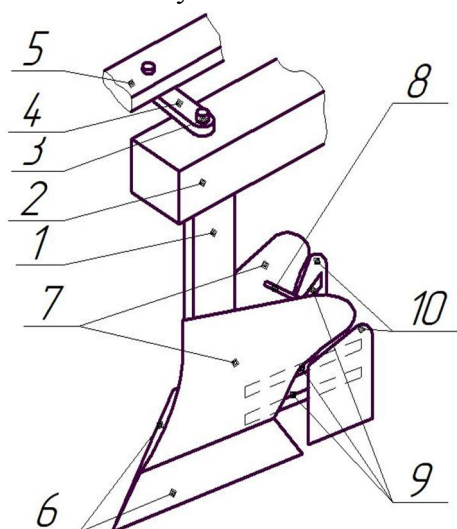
Рабочий корпус поворотного плуга: 1 – поворотная стойка; 2 – балка рамы; 3 – ось поворота стойки; 4 – кривошип стойки; 5 – шатун; 6 – лемеха; 7 – отвалы; 8 – распорка; 9 – крепёжные уголки; 10 – щиты
